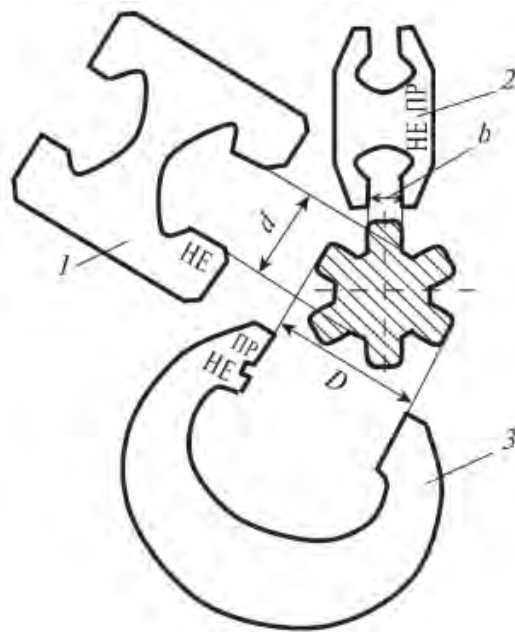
Схема поэлементного контроля шлицевого вала:
